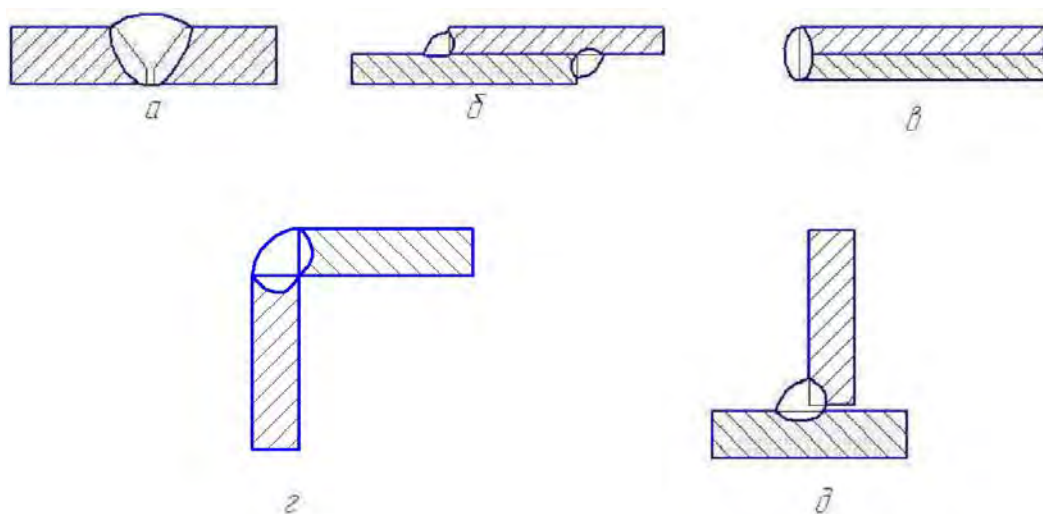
Типы сварных соединений: а – стыковое, б – нахлесточное, в – торцевое, г – угловое, д – тавровое
